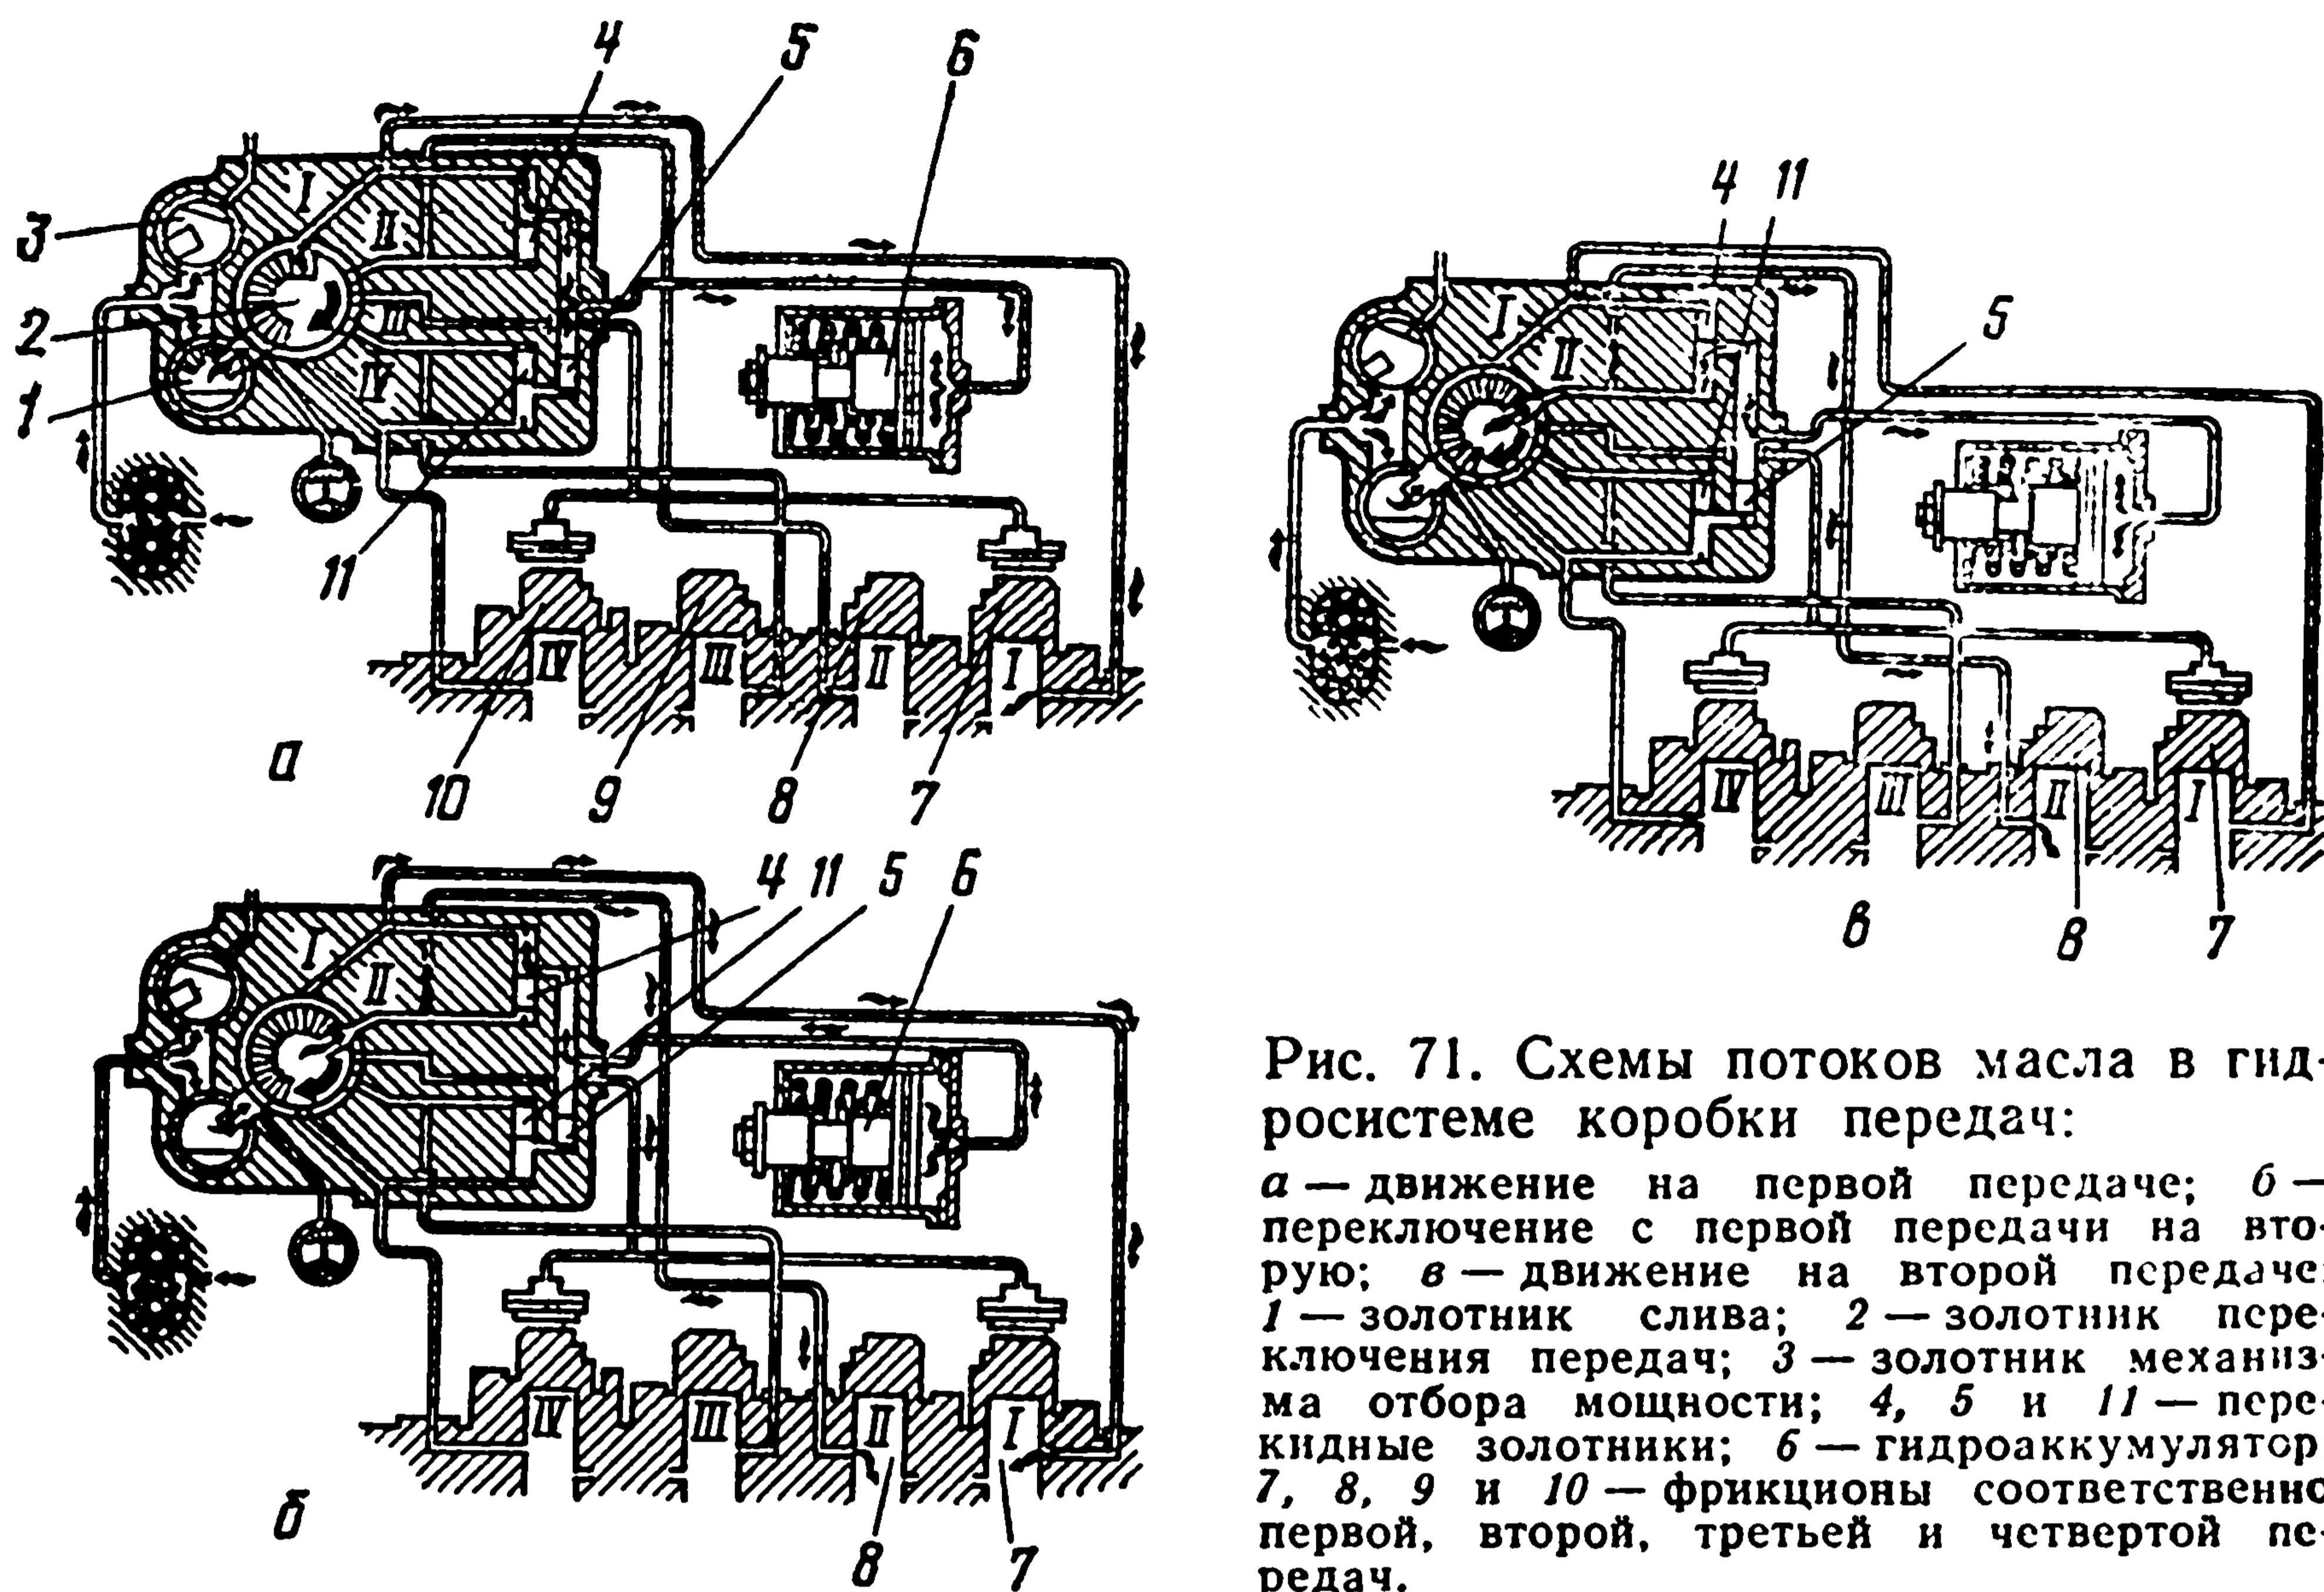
Схемы потоков масла в гидросистеме коробки передач:
